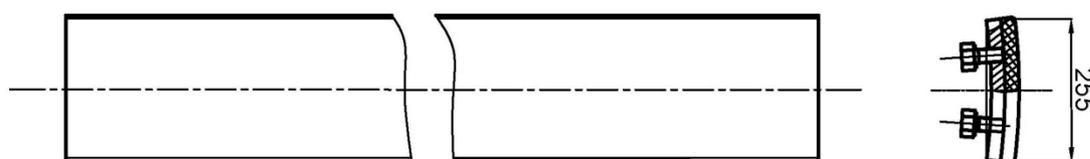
Элемент быстро съёмной резиновой футеровки приводного барабана
